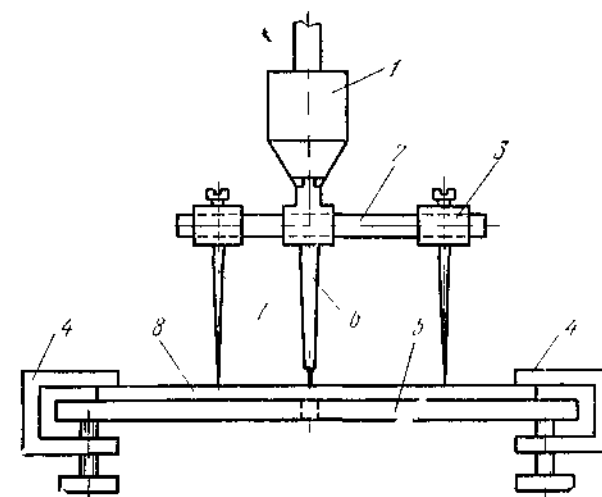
Схема приспособления для вырезания резиновых уплотнительных колец прямоугольного сечения:
